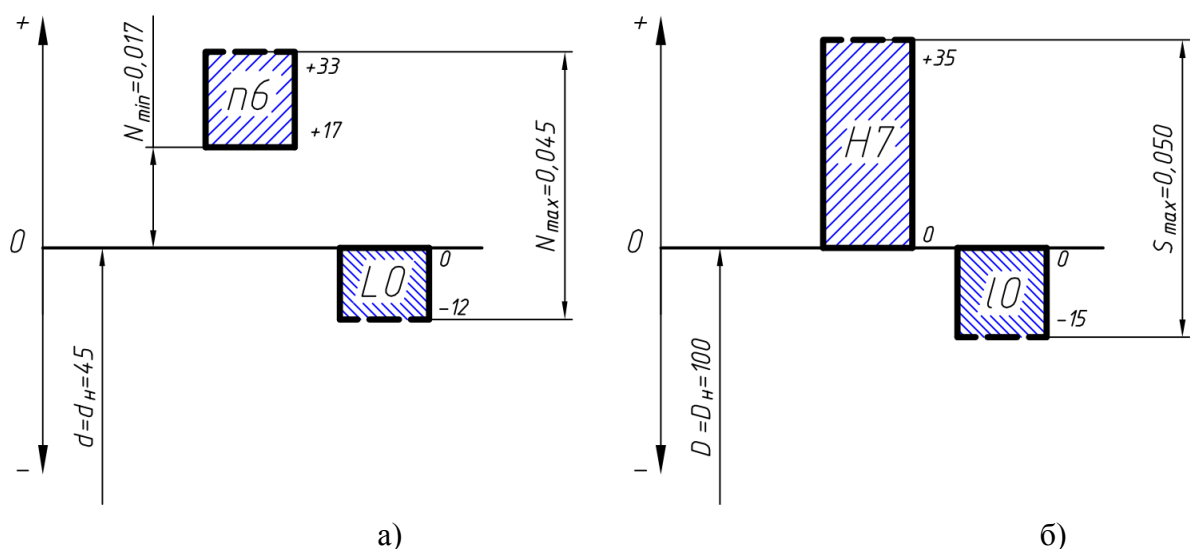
Схемы интервалов допусков посадок для соединений
